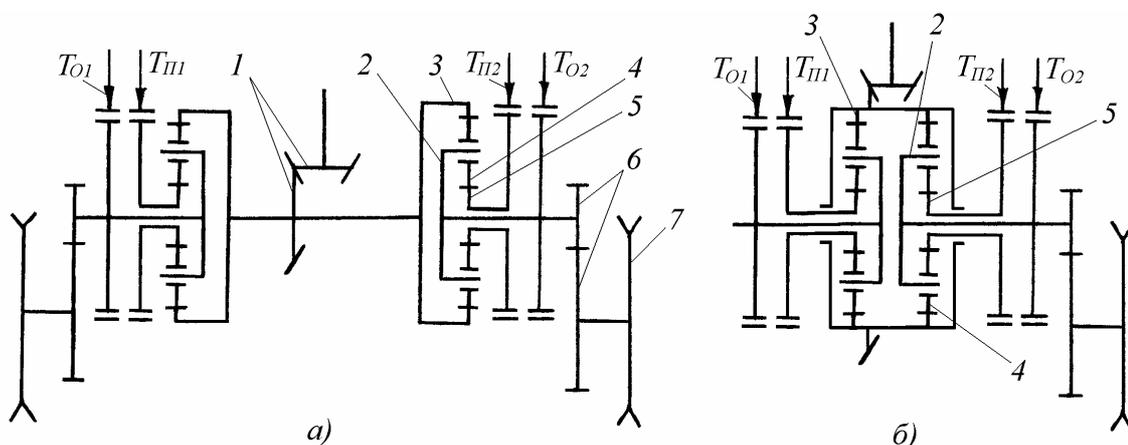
Одноступенчатый планетарный механизм поворота:
